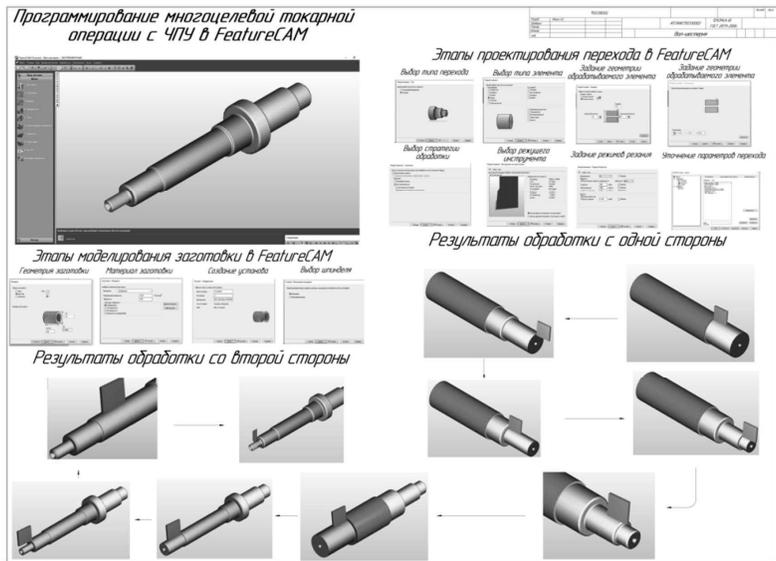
Обработка ДСЕ вал-шестерни на станке с ЧПУ
